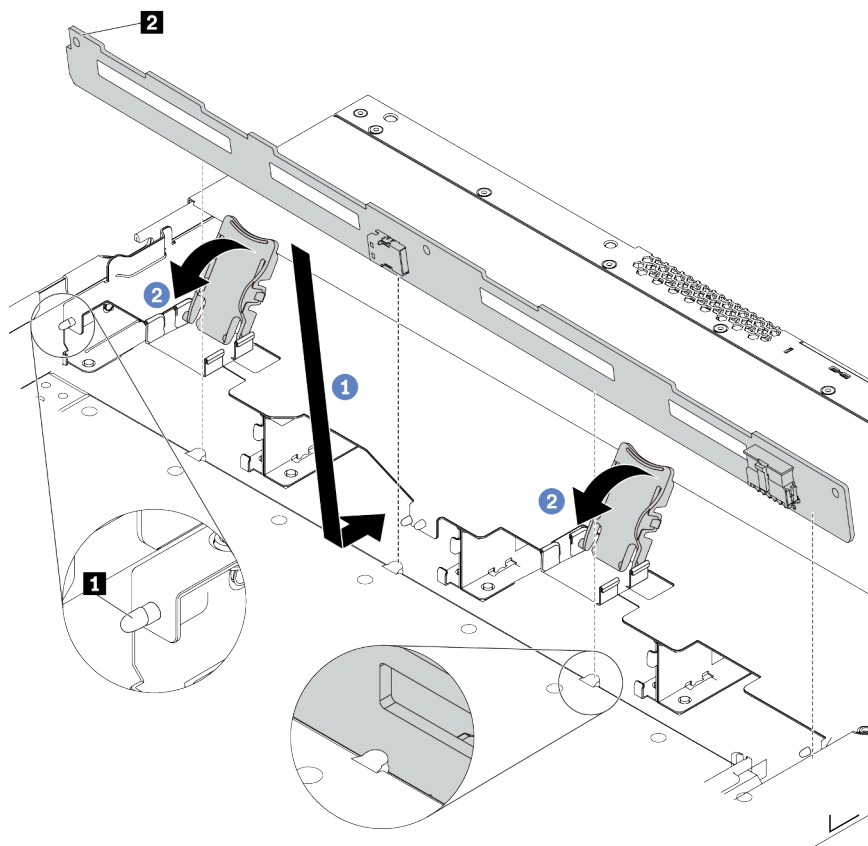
Installation du fond de panier pour quatre unités remplaçables à chaud 3,5 pouces
